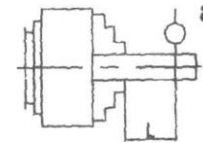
Токарный патрон с креплением за внешнюю поверхность заготовки с прямыми кулачками
